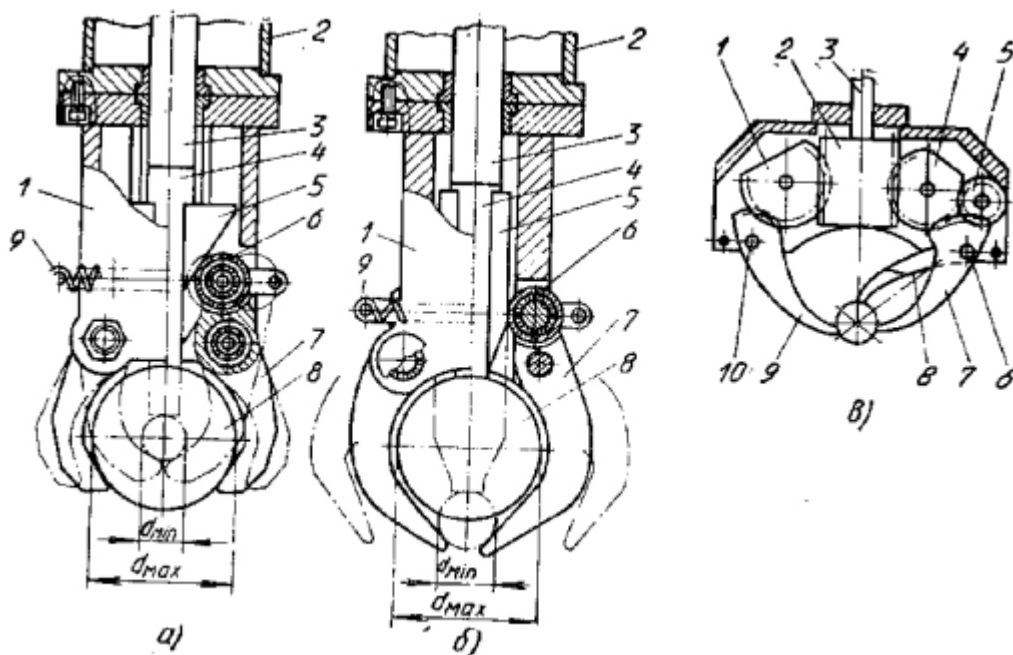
Центрирующие захватные устройства с тремя губками: а – для установки заготовок в центрах; б – для установки заготовок в призму; в – с губками специального профиля.
